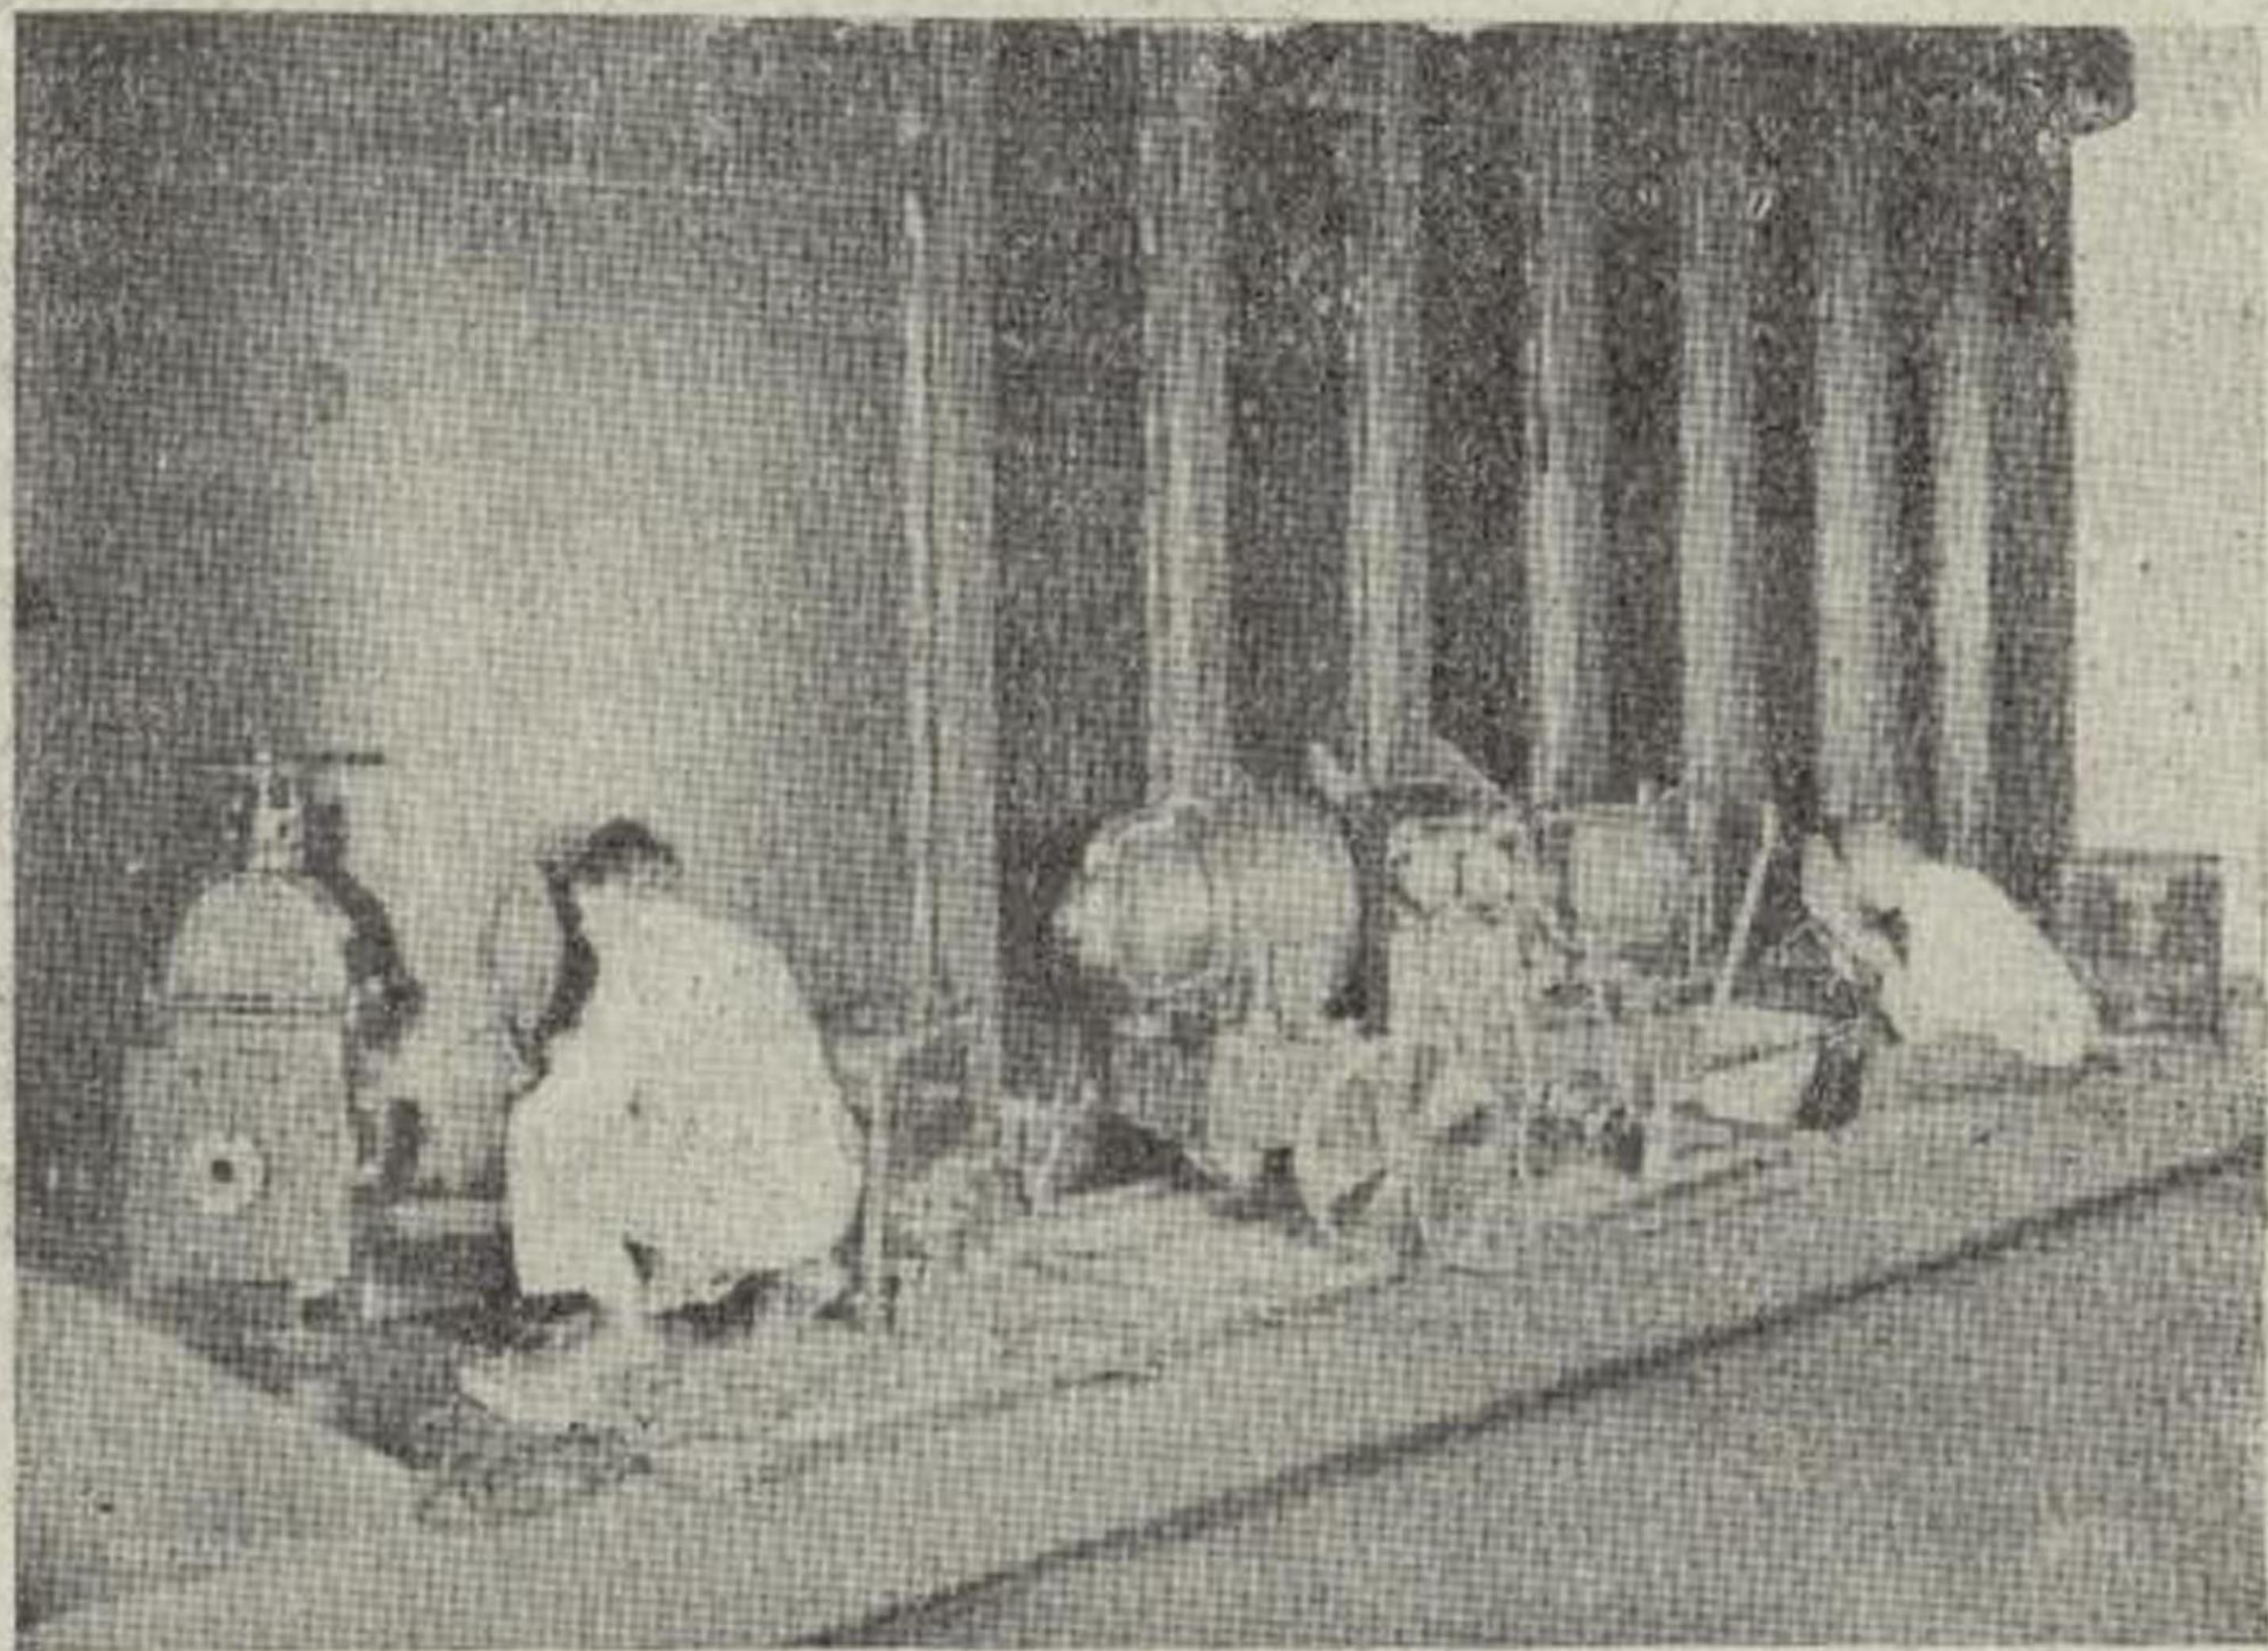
^a—Grupo de soldadura universal para dos soldadores.
